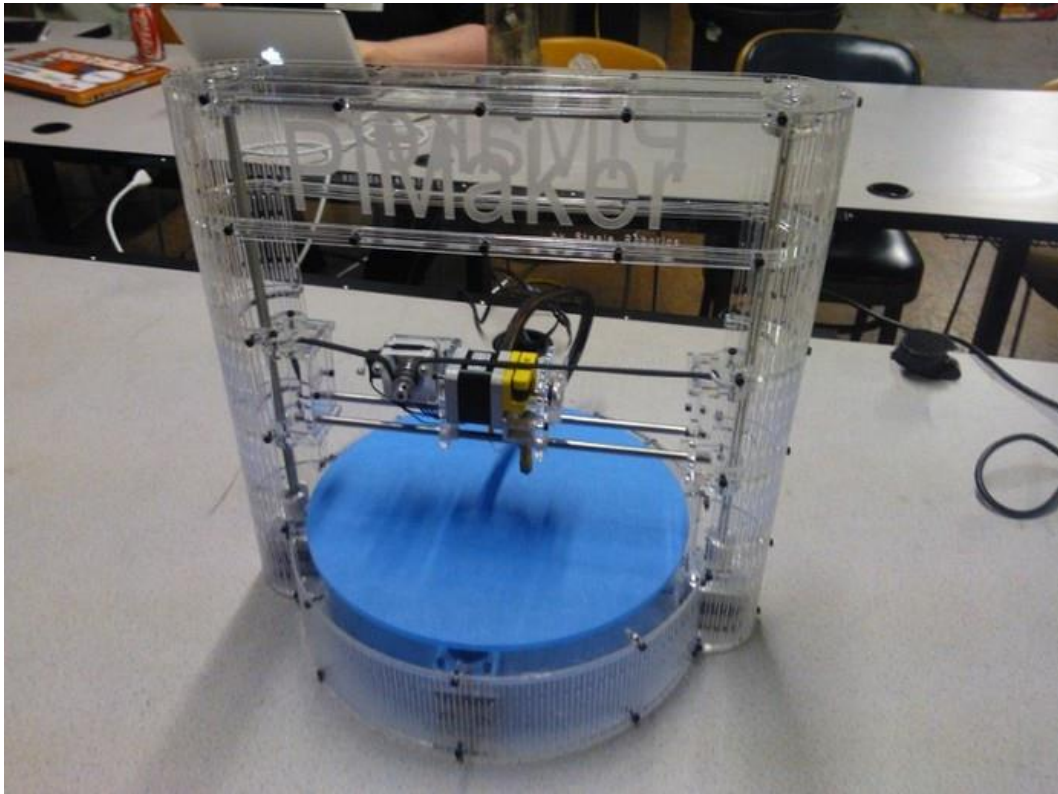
Полярний 3D принтер Pimaker 3D
